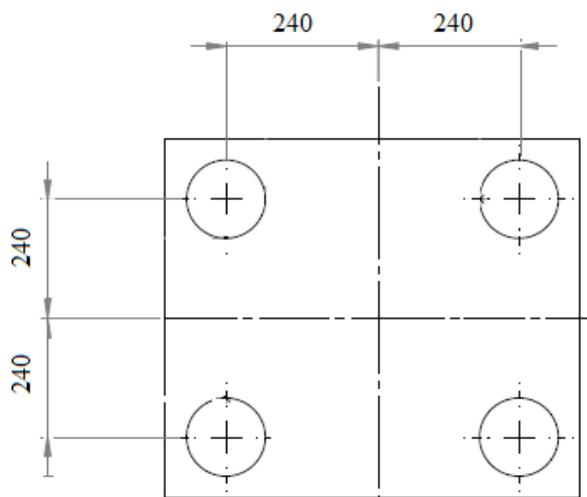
Schéma d'un plateau d'une presse 180T.
